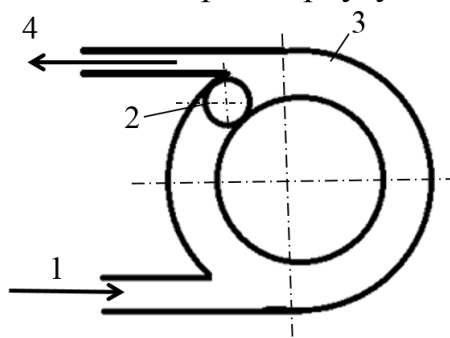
Кульковий пневматичний вібровозбуджувач (1 – сопло; 2 – кулька; 3 – кільцева доріжка; 4 – отвір для випуску повітря)
